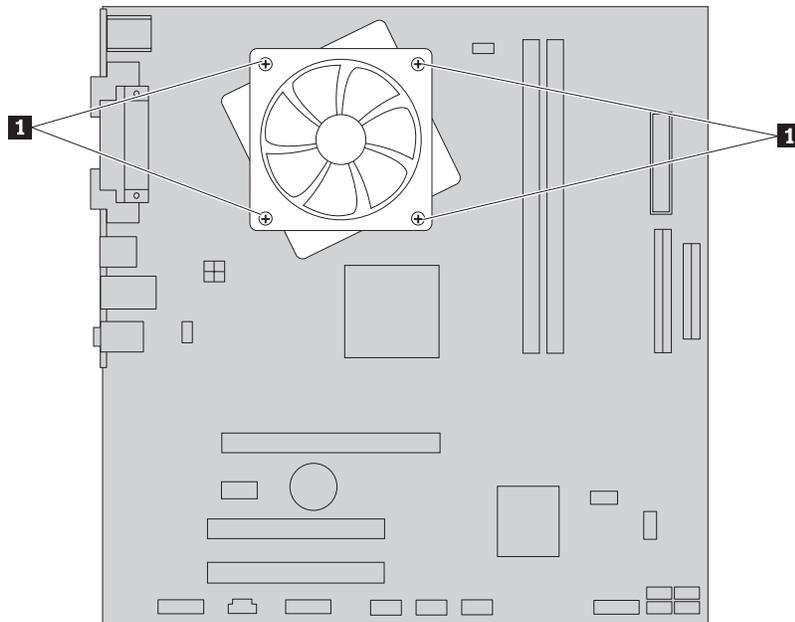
Mit Schrauben befestigten Kühlkörper entfernen
